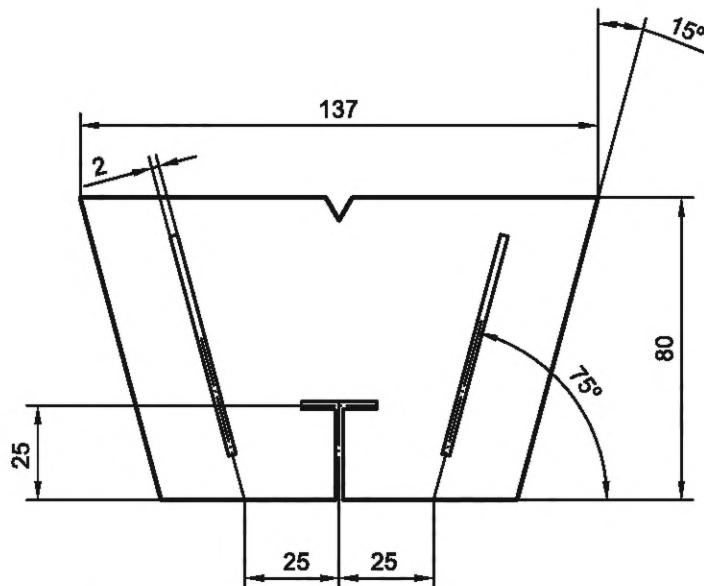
Латунный шаблон толщиной от 2 до 3 мм для подготовки образцов
